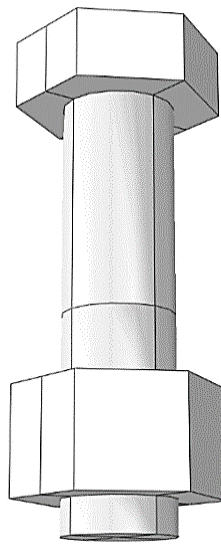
Conjunto tornillo-tuerca finalizado.
